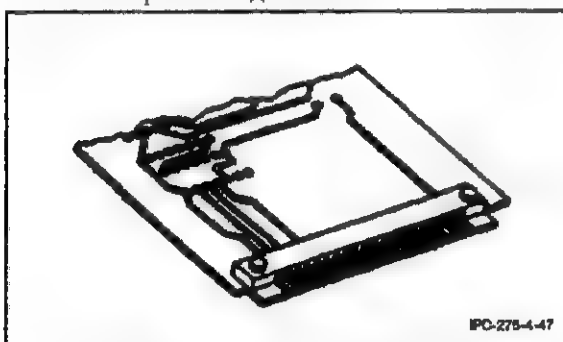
Торцевой адаптерный соединитель для печатной платы
